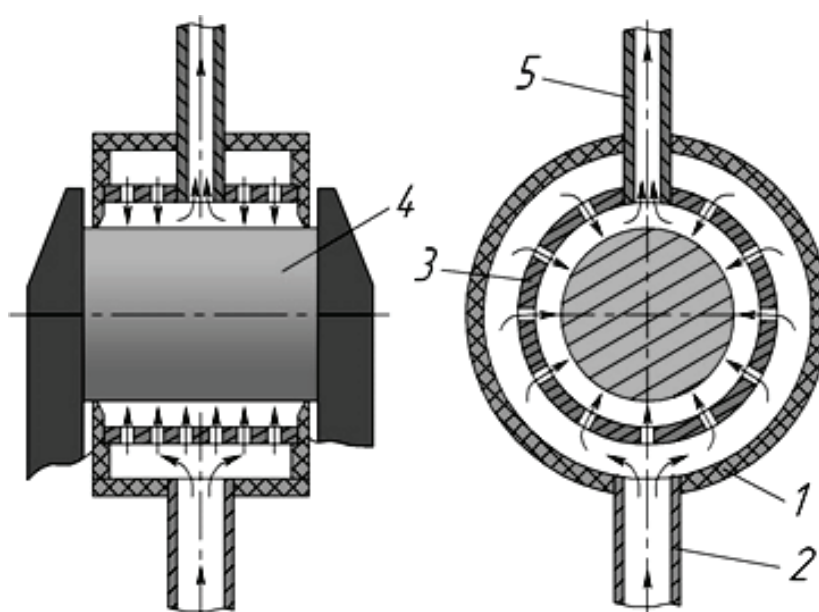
Схема вневаннового струйного железнения шейки коленчатого вала:
